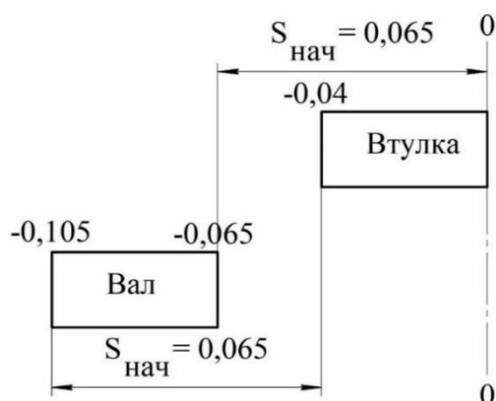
Схема расположения полей допусков при цифровом подборе соединения «распределительный вал – втулка» двигателя ЯМЗ-236
